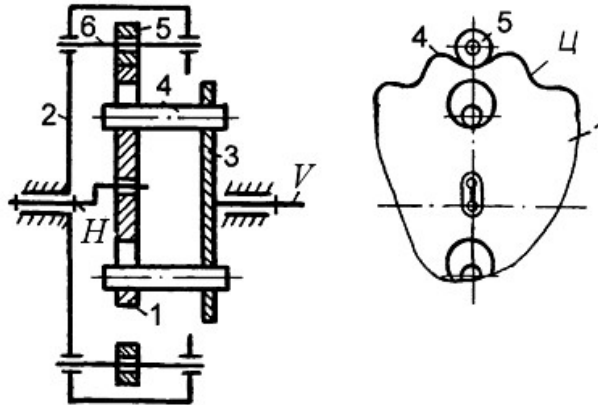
Планетарно-цевочный редуктор схемы *K-H-V
